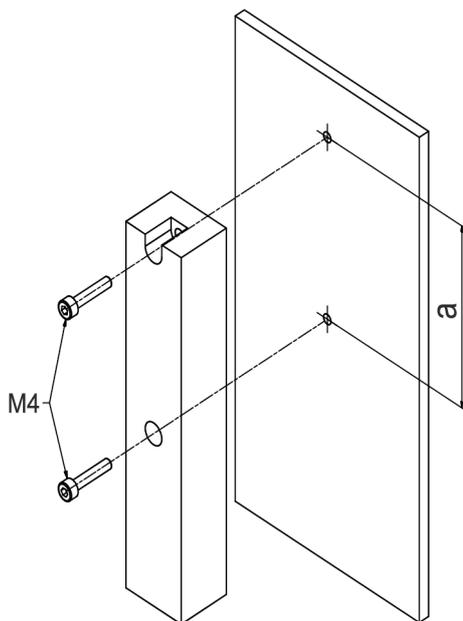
Montage mit zwei Befestigungsschrauben M4
